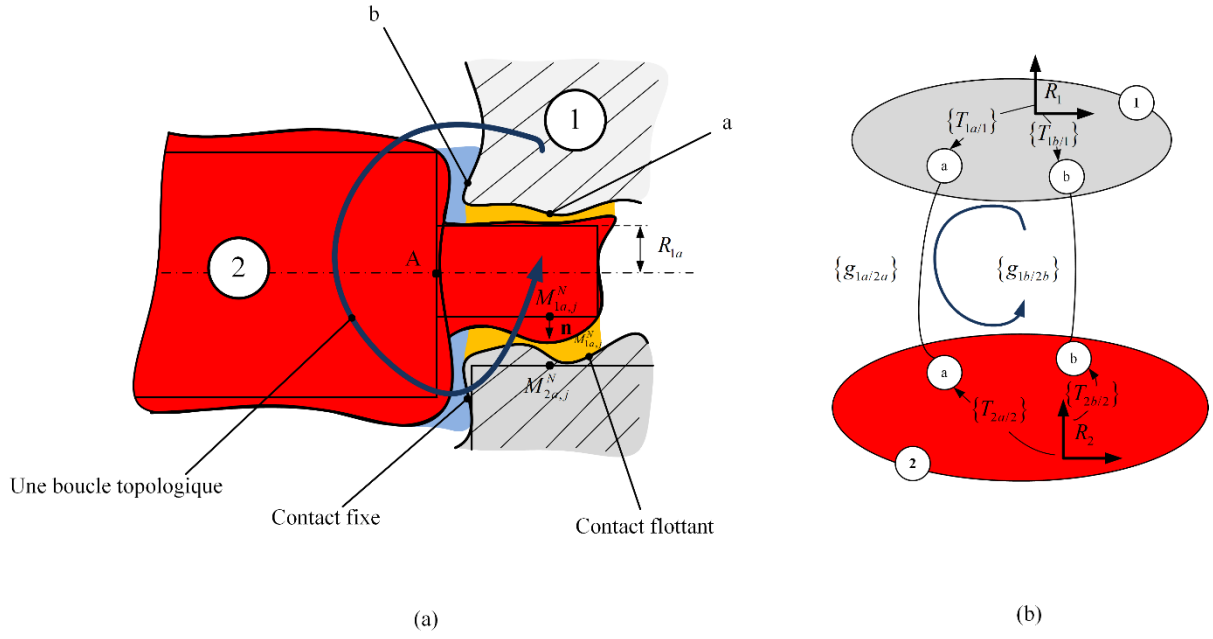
(a) Assemblage entre deux pièces ; (b) Graphe des liaisons de l'assemblage
